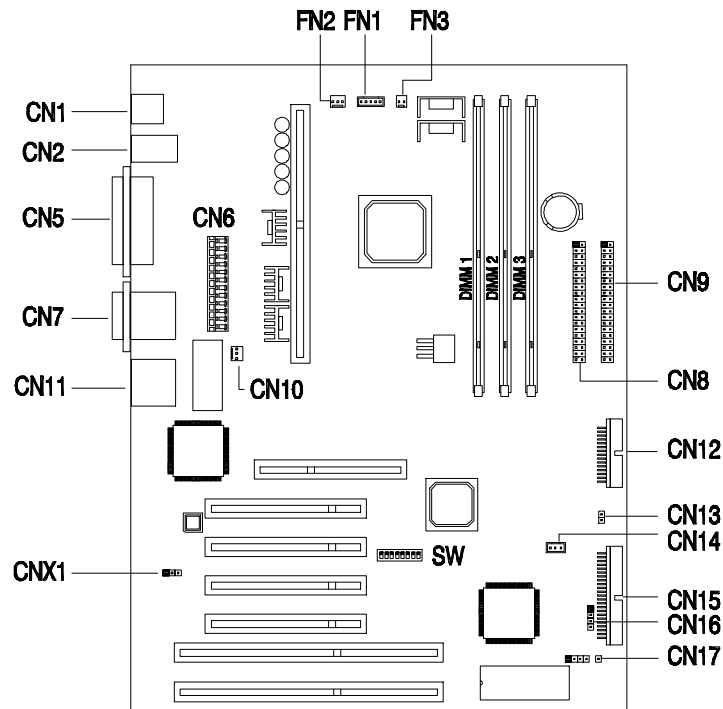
Positionen der Jumper und Steckanschlüsse
